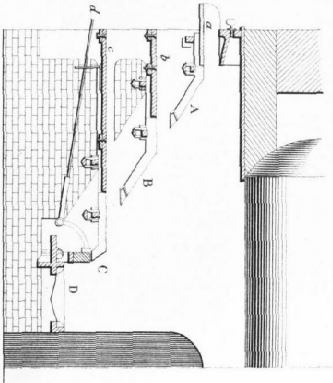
Grille à Gradins de M. de Marseille et Chodzinski.
